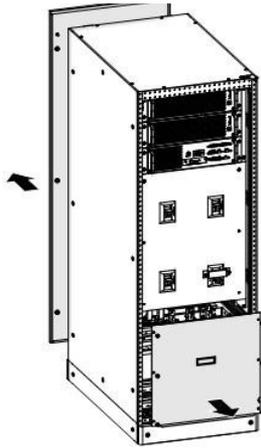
Retire la placa de cubierta de cableado trasera y superior de 160K, 200K
